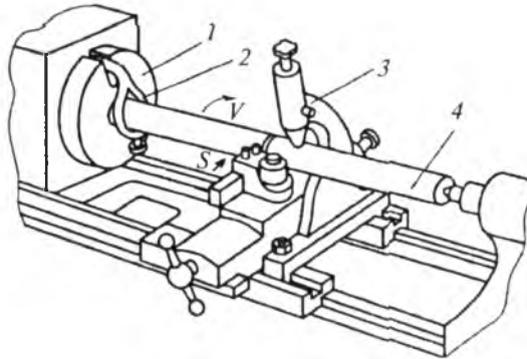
Обработка длиномерных заготовок с использованием подвижного люнета:
